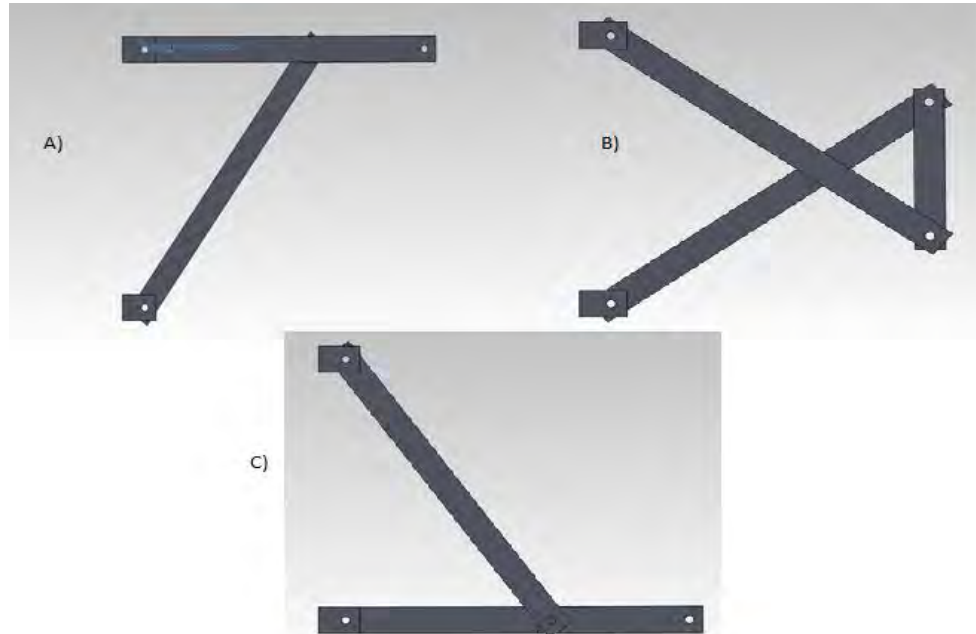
Posiciones deseadas del mecanismo, A) Inicial, B) Intemedia, C) Final.
